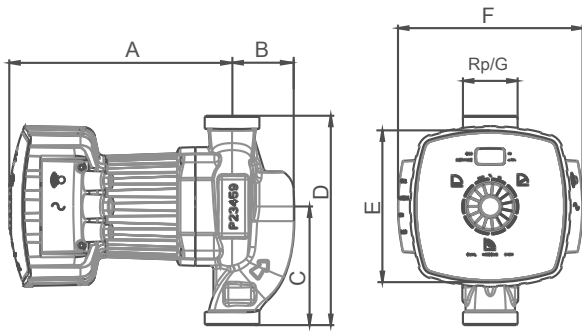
Pumpenaggregat mit Gewindeanschluss
